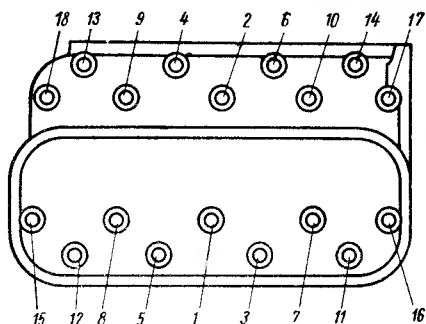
Схема последовательности затяжки гаек, крепящих головки цилиндров двигателя ЗМЗ-53
